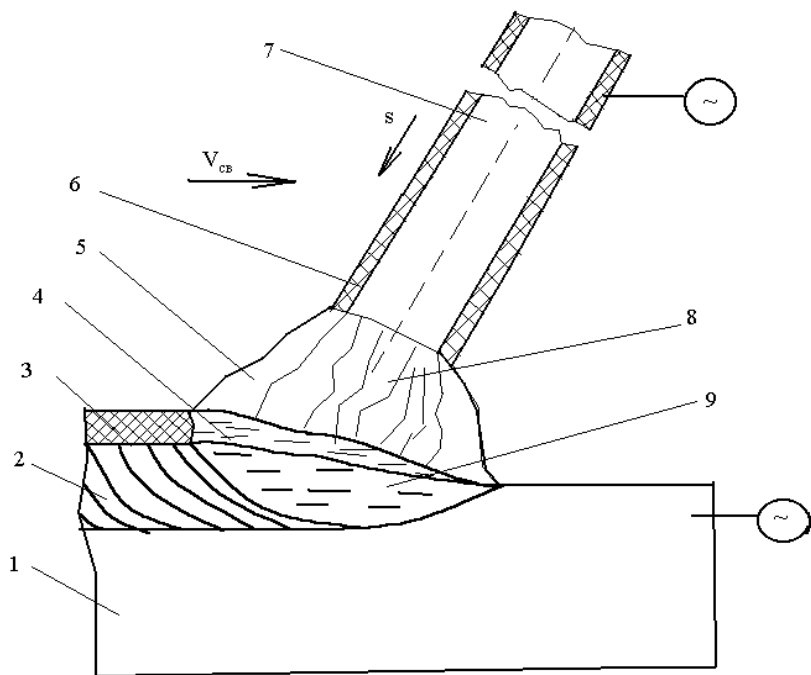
Схема дуговой сварки. 1 – деталь, 2 – сварной шов, 3 – шлаковая корка, 4 – жидкая шлаковая ванна, 5 – газовая защитная атмосфера, 6 – обмазка (покрытие) электрода, 7 – электрод, 8 – электрическая дуга, 9 – металлическая ванна
